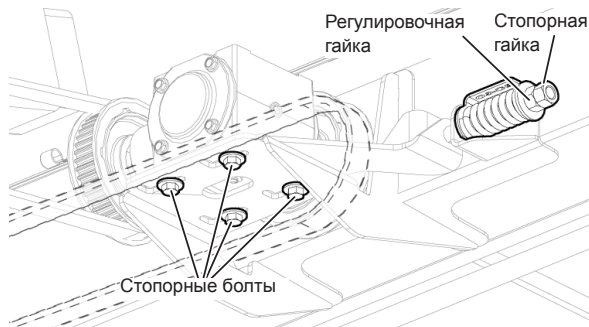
Регулировка натяжения второго ремня правого полотенного транспортера.
